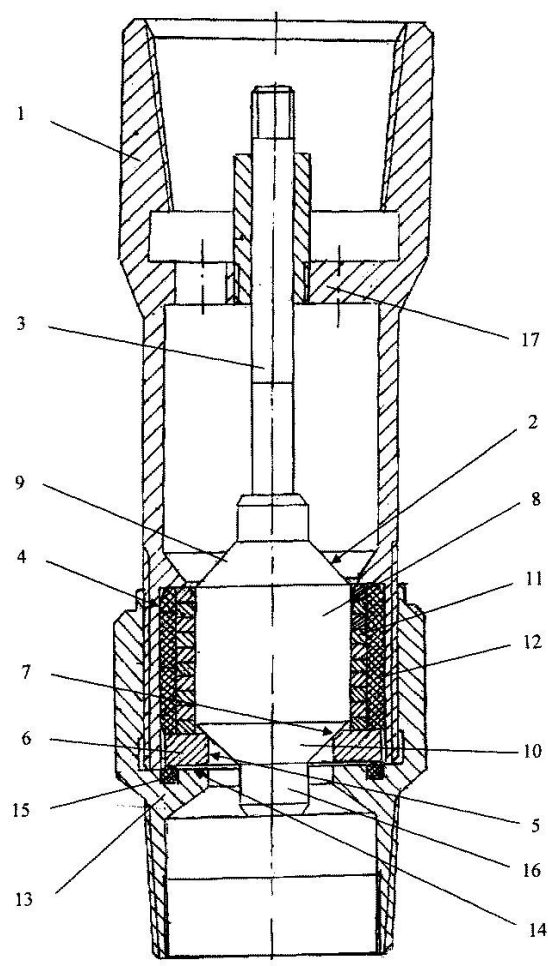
Штанговый насос с управляемыми клапанами для добычи высоковязкой нефти
